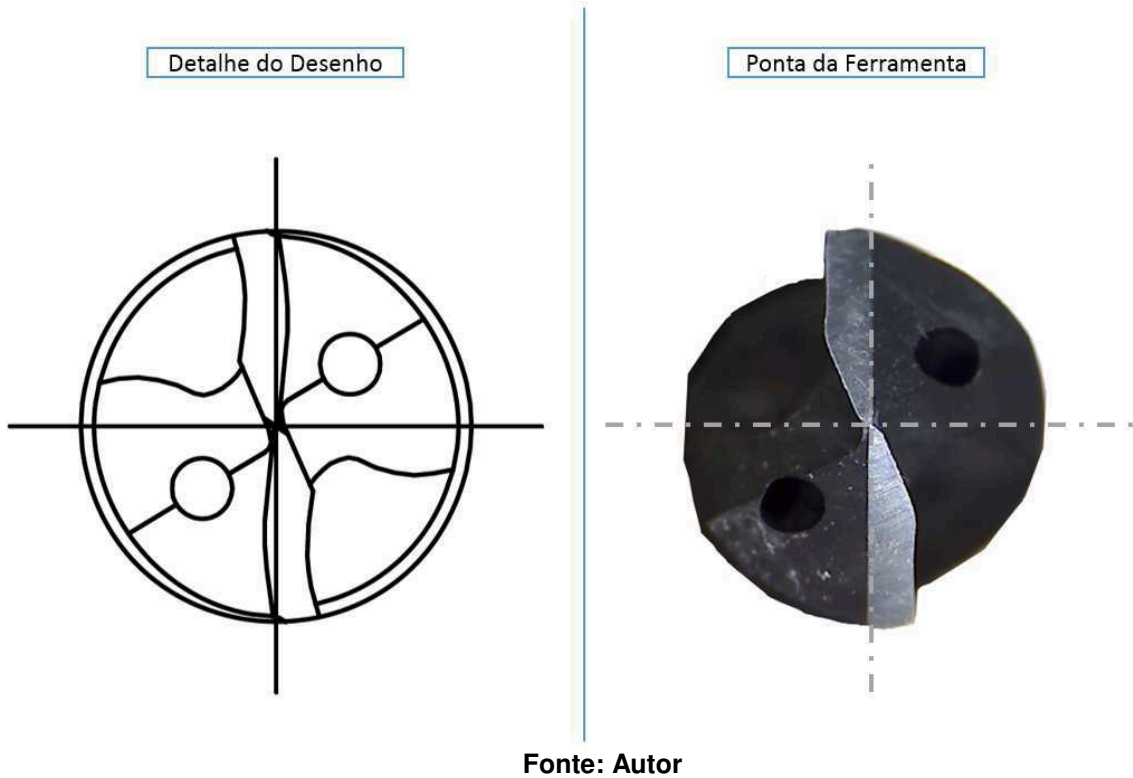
DIMENSÕES DA FERRAMENTA DE CORTE
